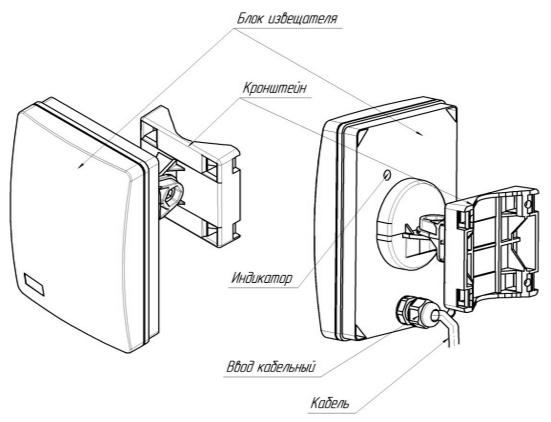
Внешний вид блока (ПРМ, ПРД) извещателя
